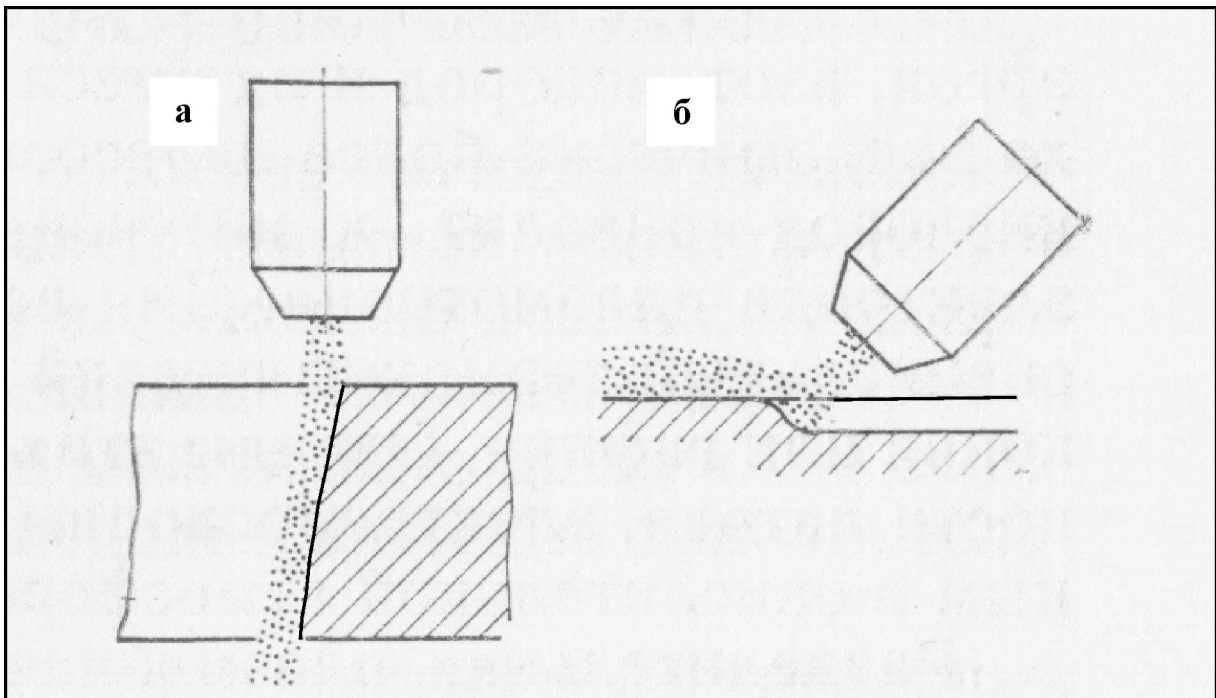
Різновиди плазмового різання: а - розділове; б - поверхневе
